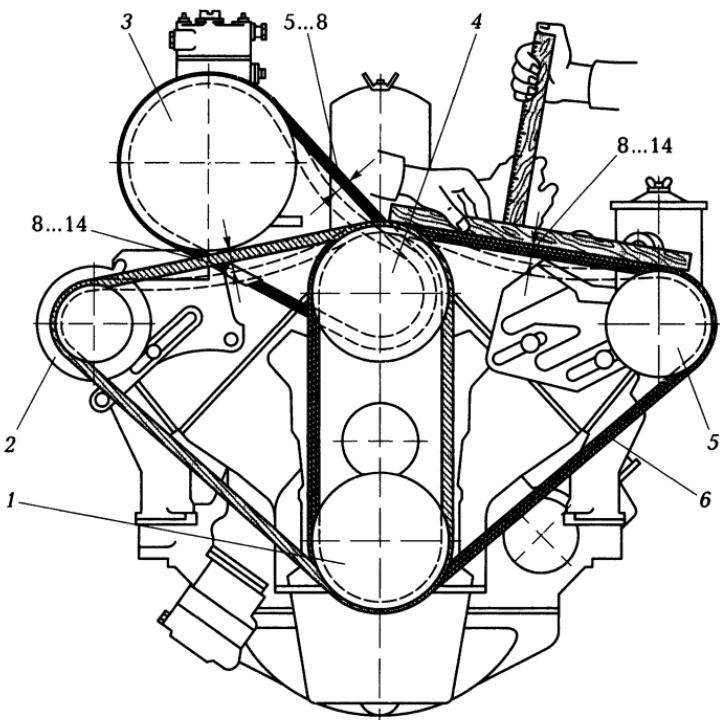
Схема проверки натяжения приводных ремней двигателя ЗИЛ-508.10:
